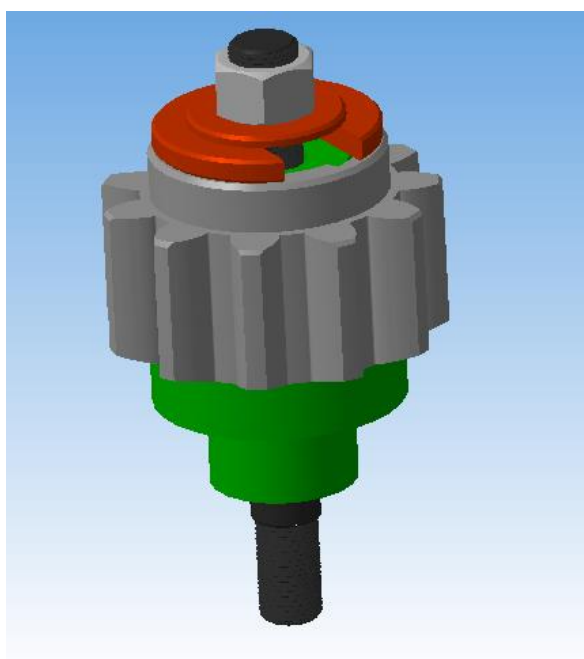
Розроблений ВП для зубофрезерної операції
